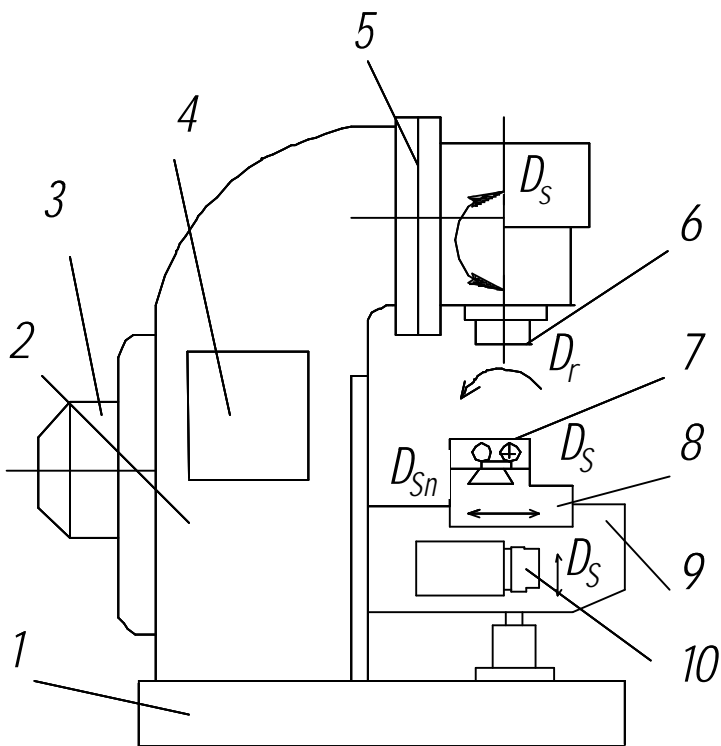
Основные узлы вертикально-фрезерного станка модели FSS450MR
